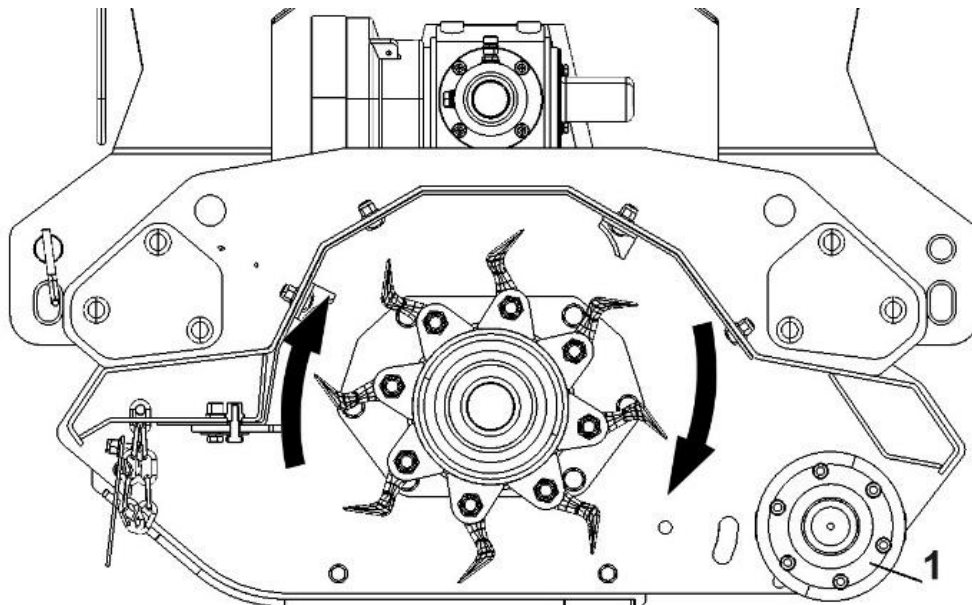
Drehrichtung der Welle mit Schlegelmessern: 1 – Tastwalze
